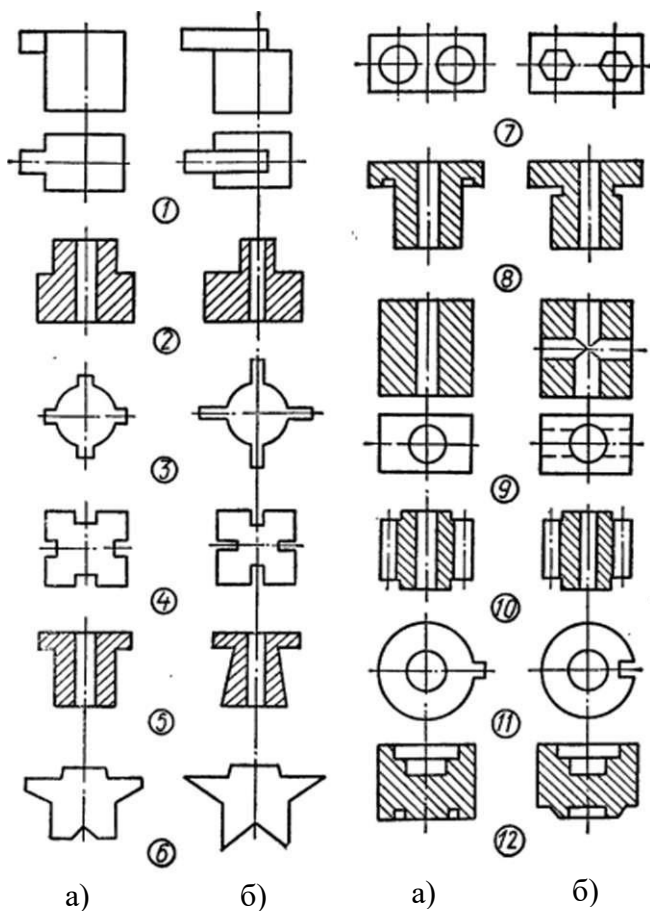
Приклади конструкцій порошкових заготовок:
